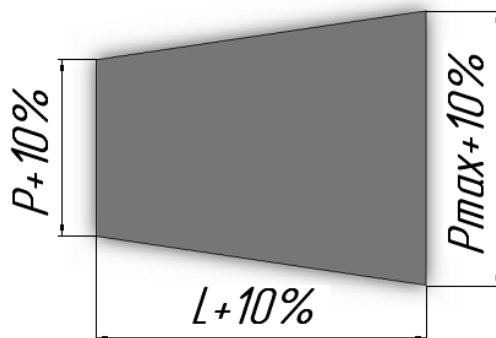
Розміри заготовки термопластичного листового матеріалу:
